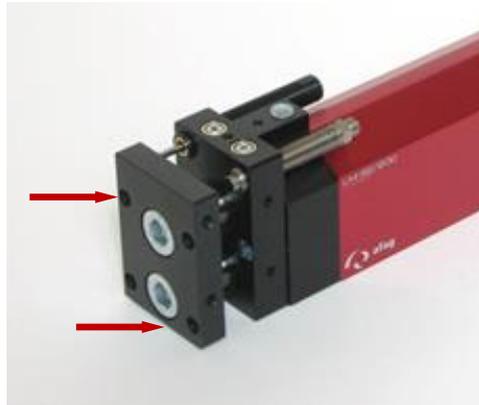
Befestigung des Linearmoduls an der Stirnplatte
